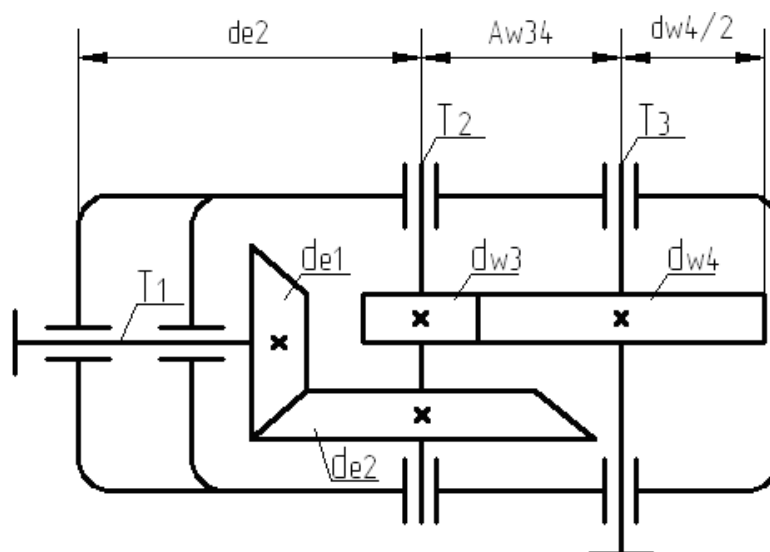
Схема коническо-цилиндрического редуктора (обозначения см. в тексте)
